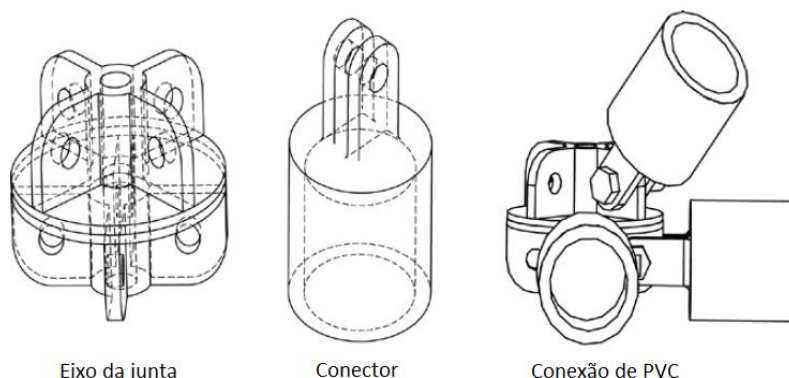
Proposta de junta de PVC para estruturas de bambu (ALBERMANI et al., 2007).
